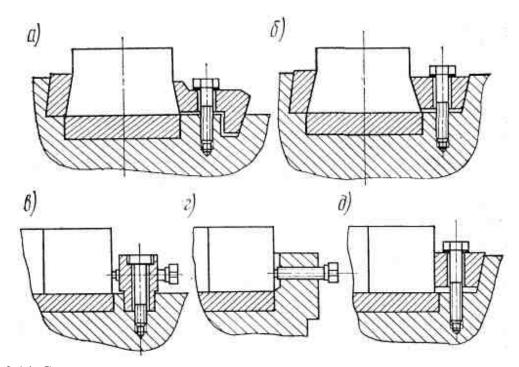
Схемы крепления вставок в пакетах штампов кривошипных горячештамповочных прессов: а — продольное накладками; б — продольное прижимными клиньями; в — боковое упорными болтами через стойку; г — боковое упорными болтами через стенку блока; д — боковое прижимными клиньями
